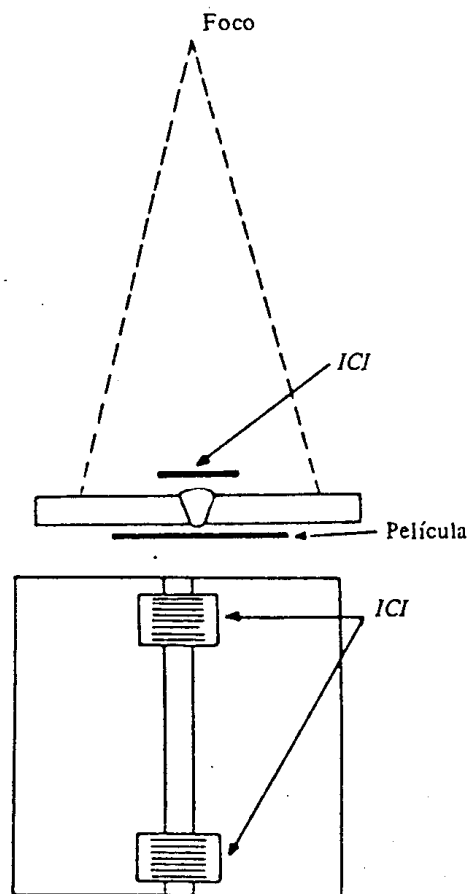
Radiografiado de soldaduras planas a tope.
